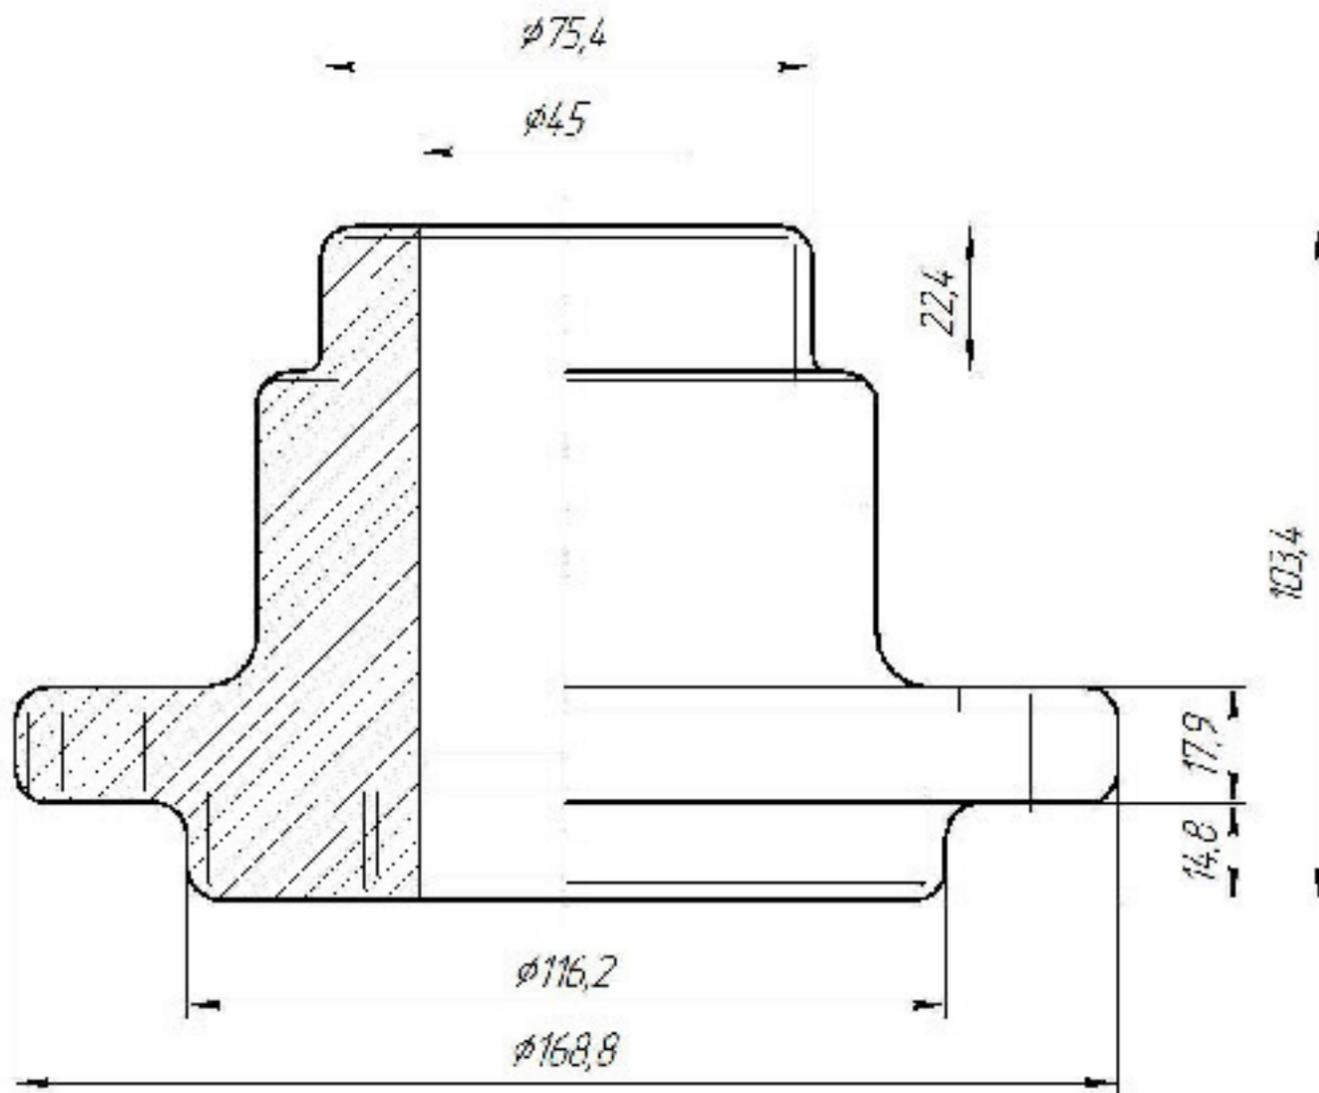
Ескіз заготовки при литті за виплавними моделями
